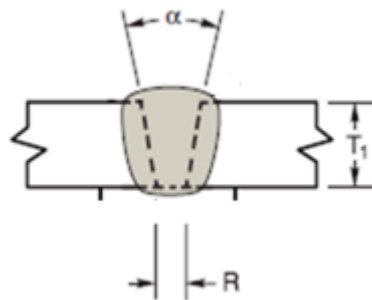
Sección de la soldadura SSW sin tacón (Fuente: www.monografias.com)
